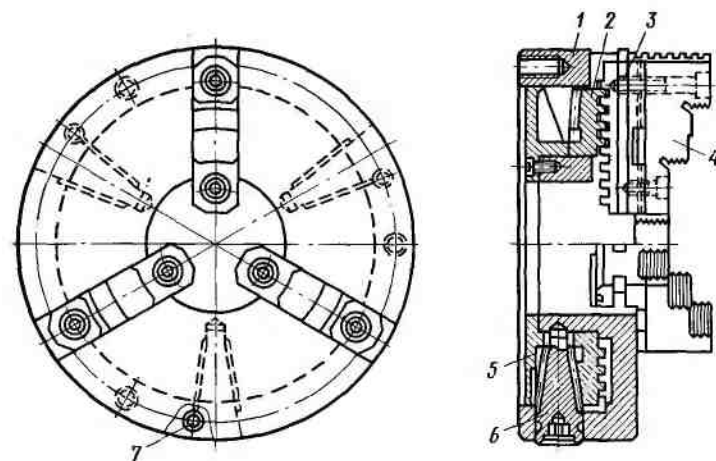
Универсальный трехкулачковый самоцентрирующий патрон:
